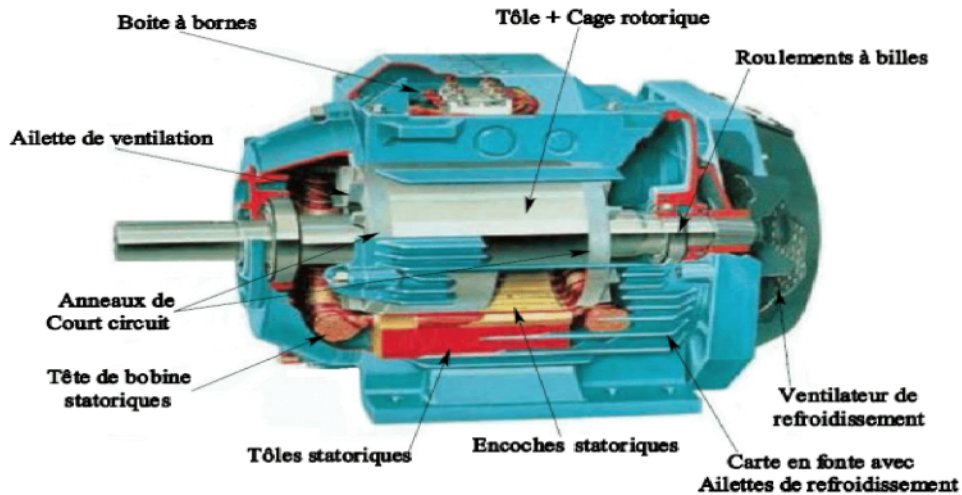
Vue d'ensemble d'une machine asynchrone à simple cage d'écureuil [4].
